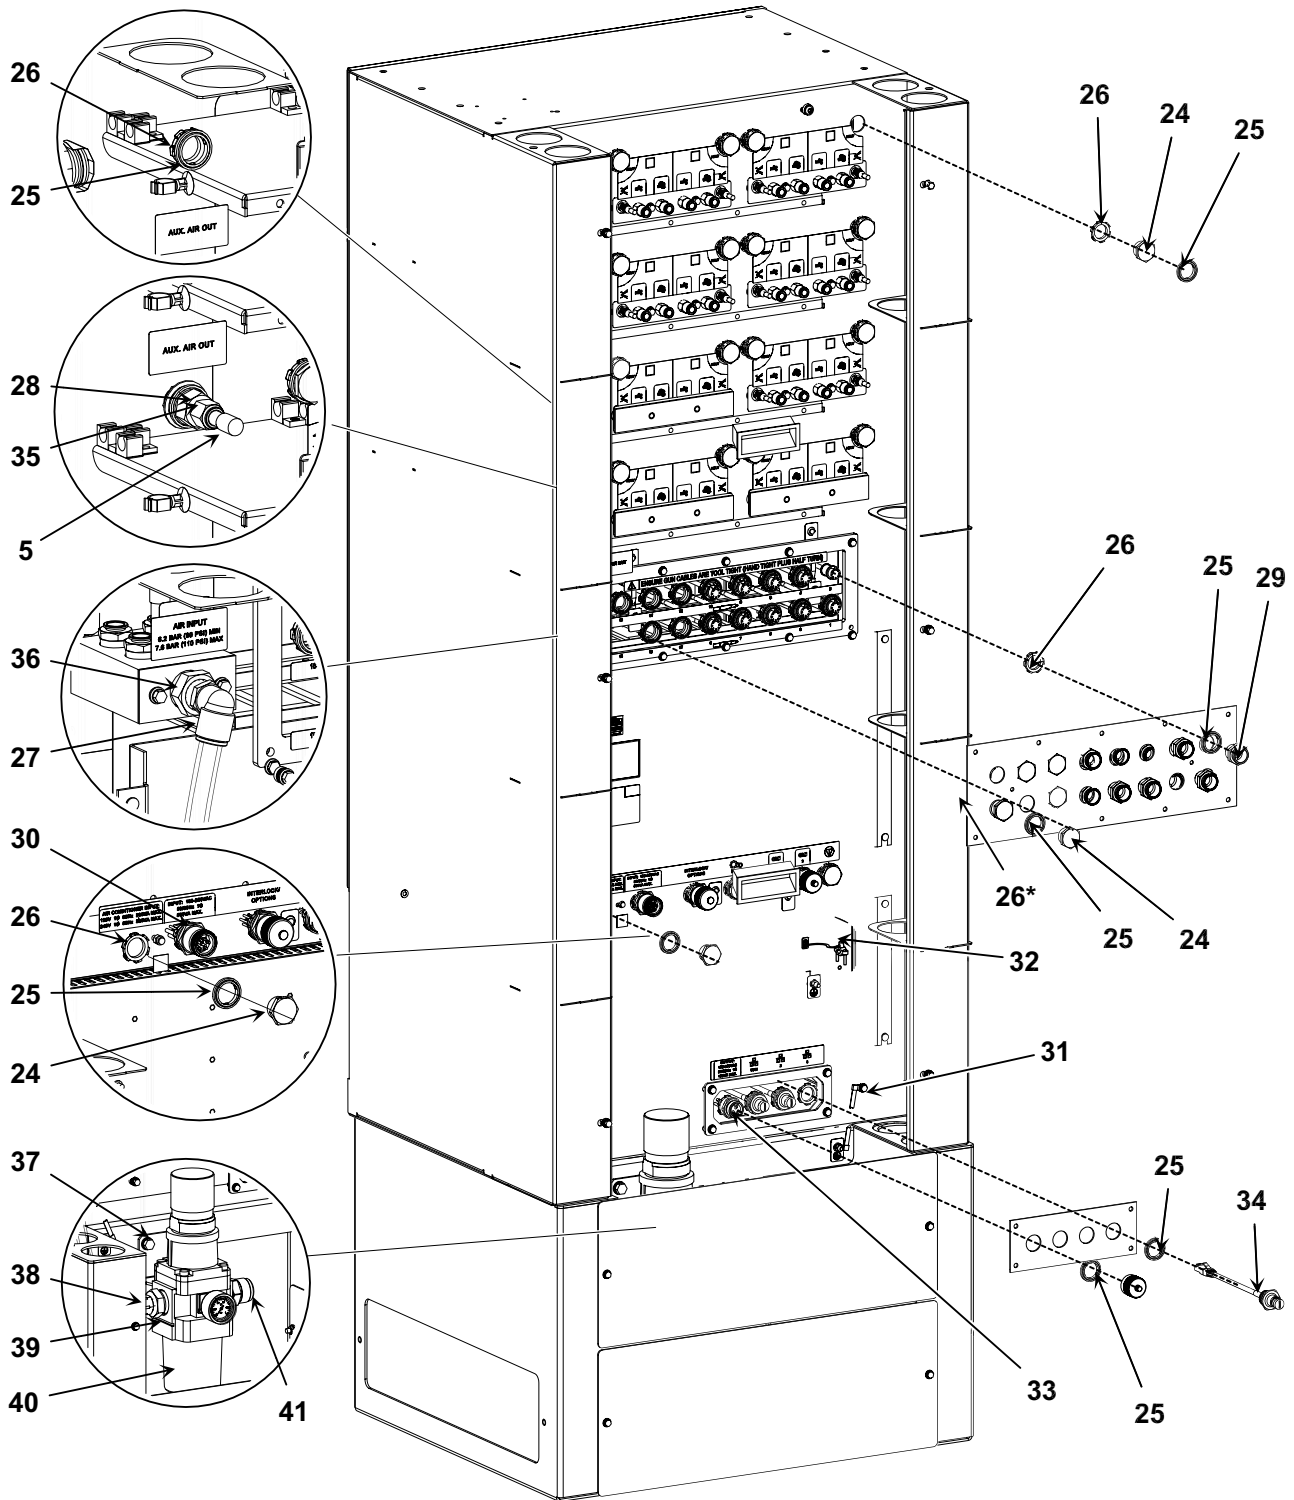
Hauptsteuerung für Komponenten der externen Anzeige, 2 von 2
